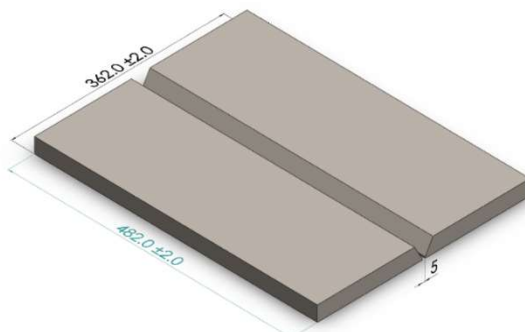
Croqui da placa de teste. Ilustração: Autor.
